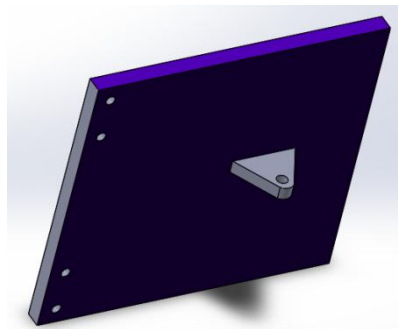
Vue en perspective de la plaque porte moteur.
